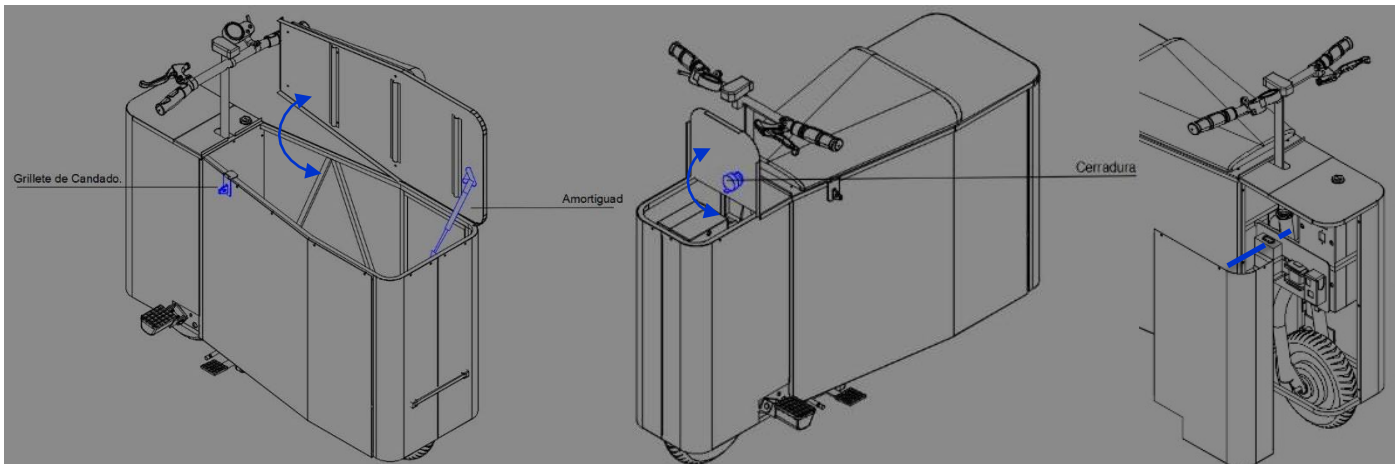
Sistema de acceso (de izquierda a derecha), puerta de acceso a paquetería, puerta para el acceso a la batería y el acceso a los componentes electrónicos y sistema de dirección.
